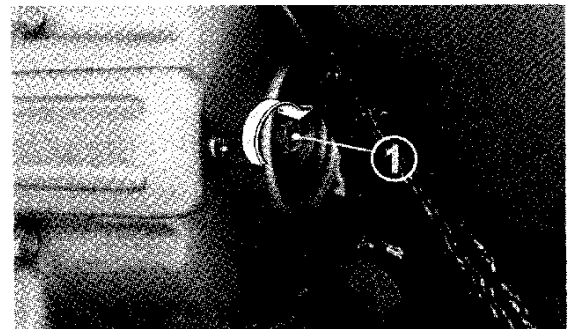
(1) Lichtmaschinenrotor-Befestigungsschraube
